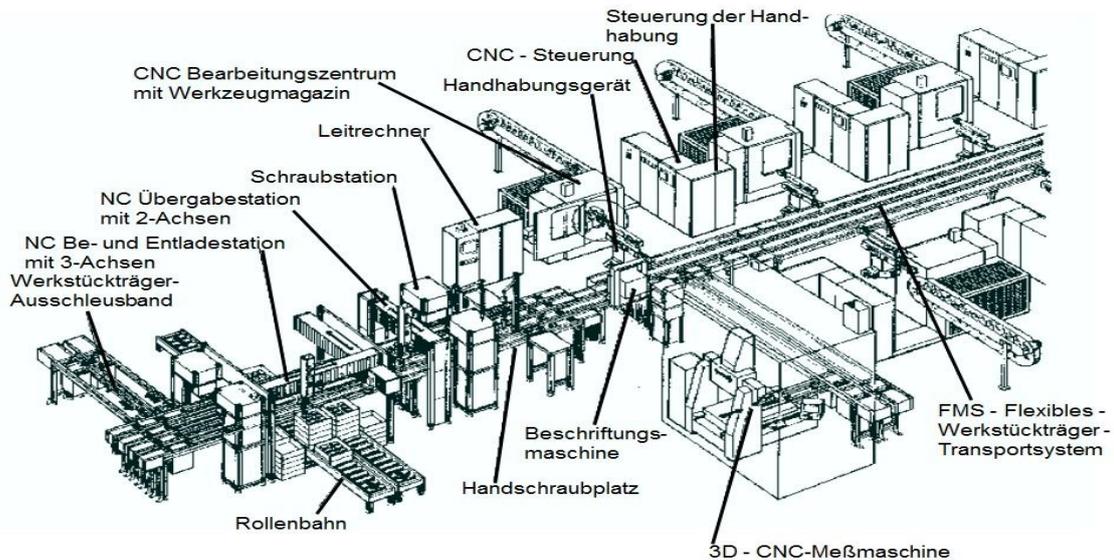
Elemente und Grundaufbau eines FFS(BOSCH Industrierausrüstung, Anwender BOSCH Stuttgart)^[1]
